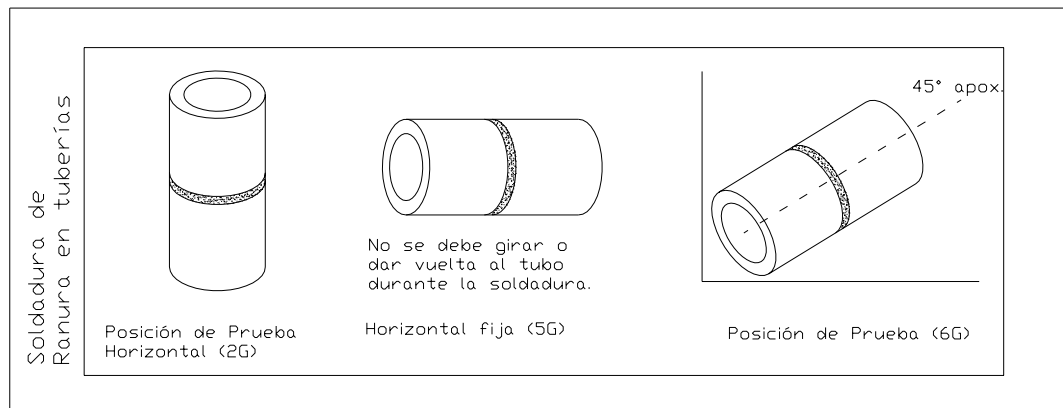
POSICIONES DE SOLDEO SEGÚN LA AWS.
